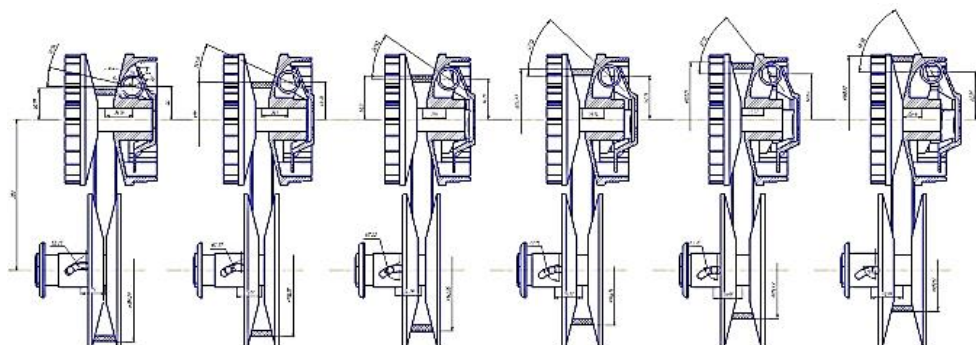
2D-чертежи шксти рабочих положений вариатора
